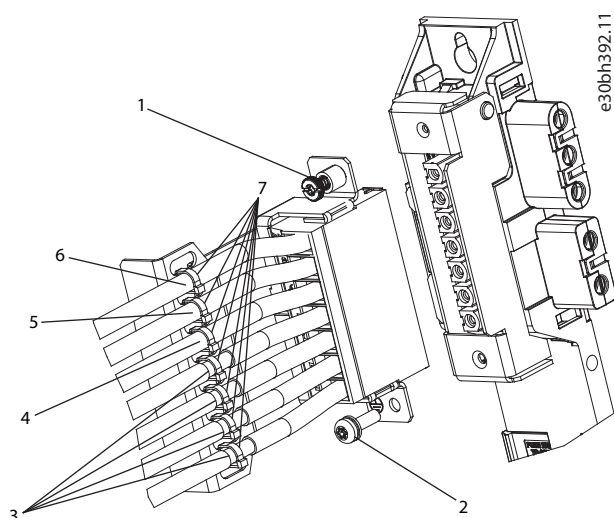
Collegamento del modulo di espansione EXM 510
